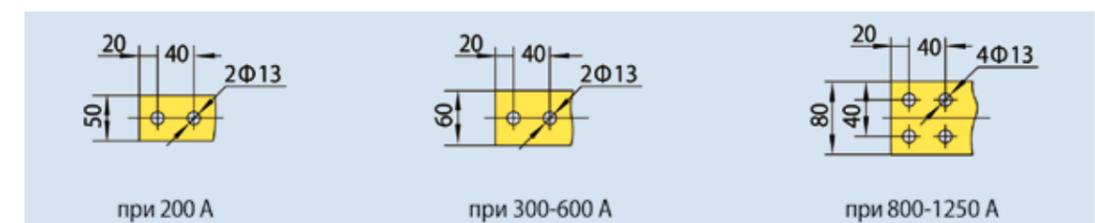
Внешний вид и размеры при 200-1250/5 А
